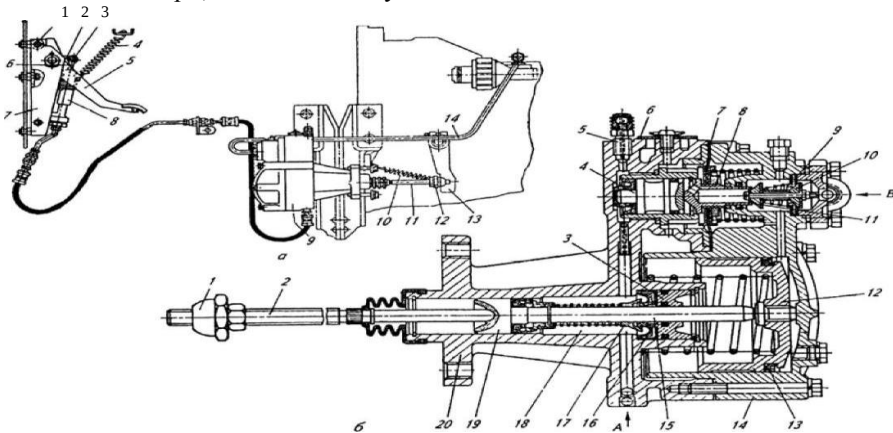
Привід зчеплення *КамАЗ-5320*: *а* - загальний вигляд приводу: 1 - обмежувач; 2 - важіль; 3 - палець; 4, 10 - пружини; 5 - педаль зчеплення; 6 - шток гідроциліндра; 7 - кронштейн; 8 - гідроциліндр; 9 - пневмогідропідсилювач; 11 - шток поршня; 12 - регулювальна гайка; 13 - важіль вала вилки; 14- повітряний шланг;*б* - пневмогідропідсилювач; 1 - сферична гайка; 2 , 15 - штоки; 3 - корпус комбінованого отвору; 4 - слідкувальний поршень; 5 - клапан видалення повітря з системи; 6 - ущільнювач випускного отвору; 7 - діафрагма слідкувального пристрою; 8 - сидло випускного клапана; 9 - сидло впускного клапана; 10 - впускний клапан; 11 - випускний клапан; 12 - поршень пневматичний; 13 - ущільнювач поршня; 14 - передній корпус; 16 - манжета; 17 - розпірна втулка; 18 - виконавчий циліндр; 19 - поршень вимкнення зчеплення; 20 - задній корпус; *А* - підведення рідини; *В* - підведення стислого повітря.
